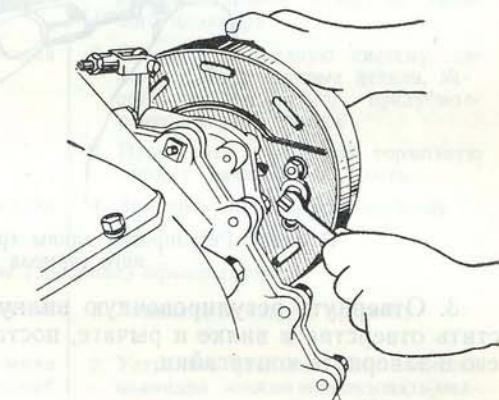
Регулировка зазоров между колодками и тормозным барабаном ручного тормоза
